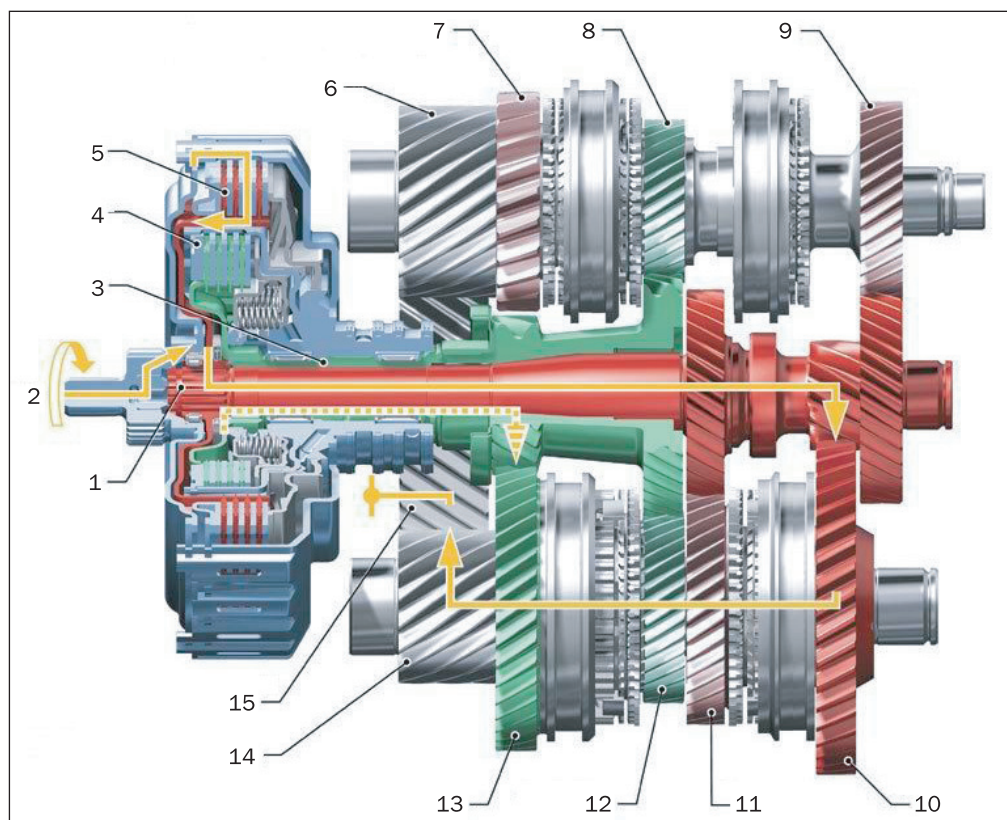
Коробка передач с двумя сцеплениями автомобиля Audi TT 3.2 Quattro: 1 — ведущий вал I; 2 — двигатель; 3 — ведущий вал II; 4 — сцепление II; 5 — сцепление I; 6 — выход на главную передачу; 7 — задний ход; 8 — VI передача; 9 — V передача; 10 — I передача (активна); 11 — III передача; 12 — IV передача; 13 — II передача (выбрана); 14 — выход на главную передачу; 15 — главная передача
